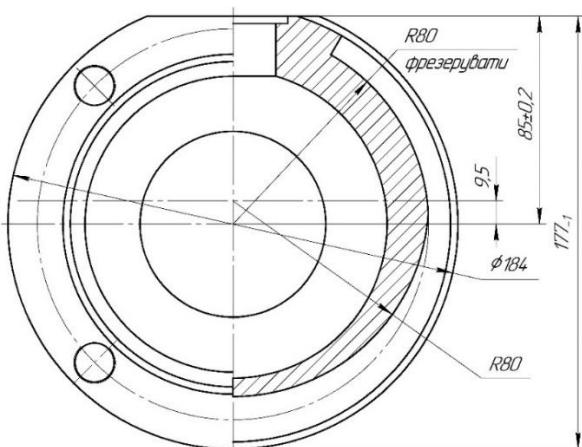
Нетехнологічний елемент деталі – ексцентрична поверхня
